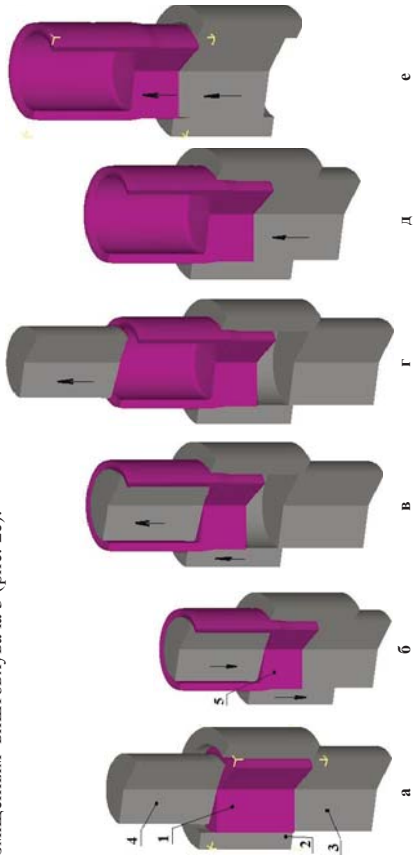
Розрахункові схеми в розрізі для ЗВР заготовки діаметром  $D_0 = 50$  мм
